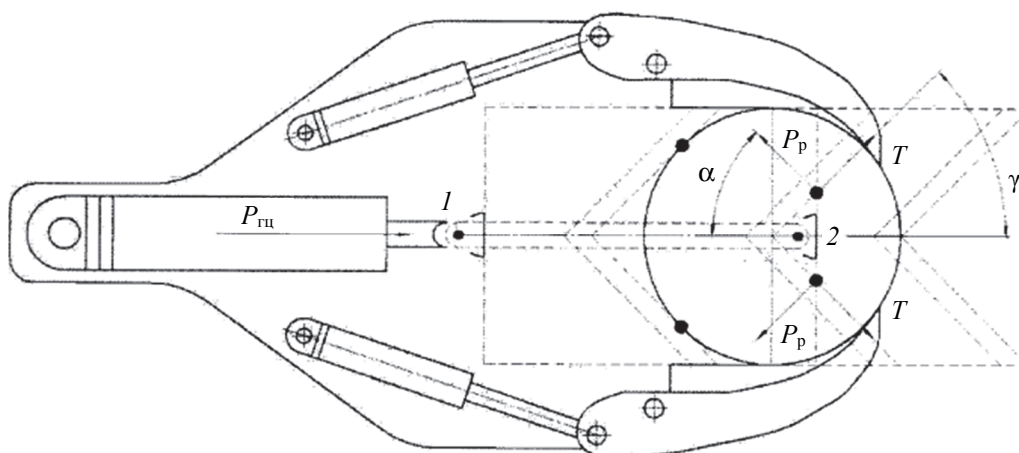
Компановочно-кинематическая схема одноножевого срезающего устройства типа гильотина: 1 – гидроцилиндр для привода ножей; 2 – толкатель;
